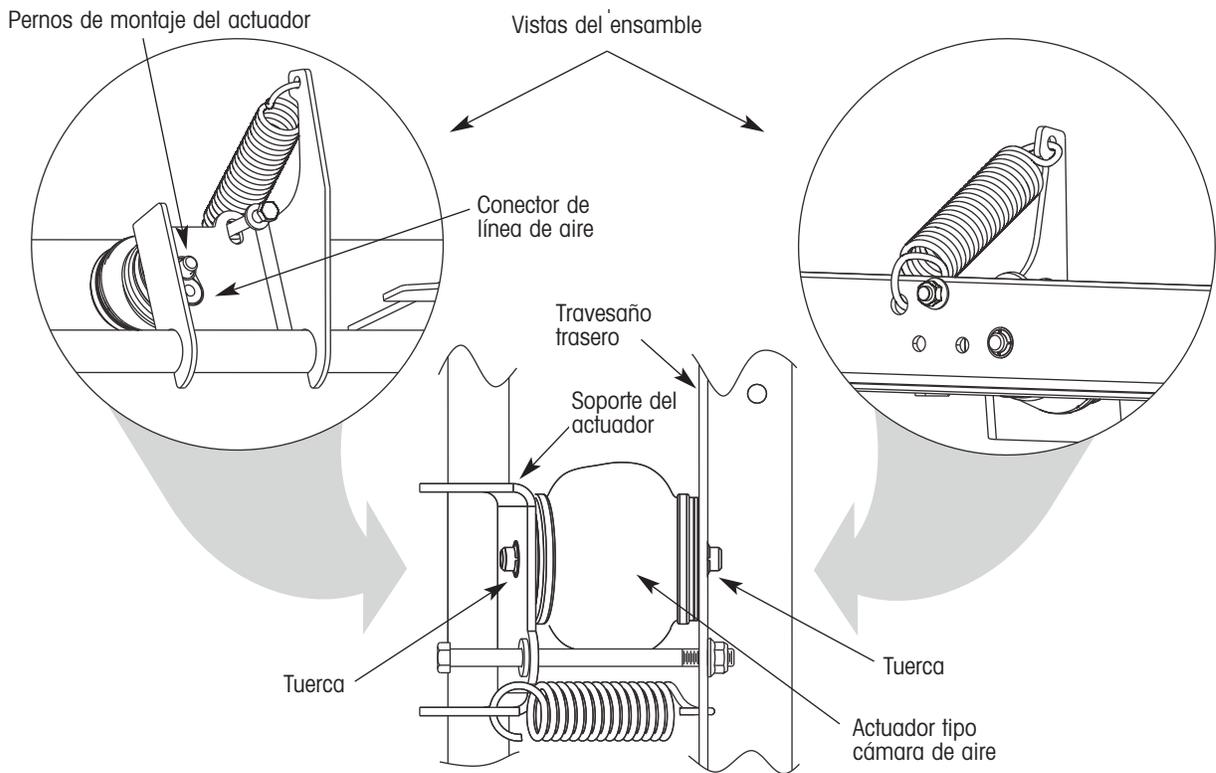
Detalles de instalación del actuador tipo cámara de aire
